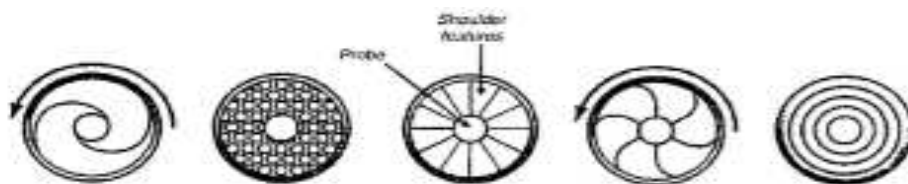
Des exemples de profils (de type rainures ou spirales). [17]
